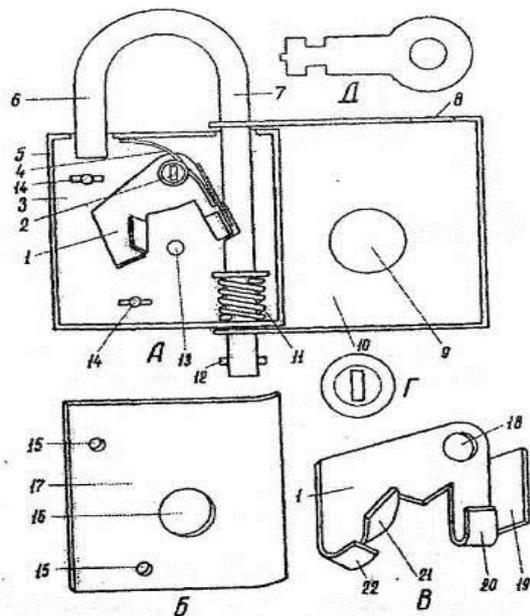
Устройство висячего бессувальдного контрольного замка: А - замок; Б - крышка корпуса; В - засов; Г - ключевина; Д - ключ; 1 - хвостовик засова; 2 - ось засова и пружины; 3 - основание корпуса; 4 - пружина засова; 5 - боковая стенка; 6 - свободный конец дужки; 7 - запираемый конец дужки; 8 - отверстие для свободного конца дужки; 9 - контрольное окно; 10 - дополнительная (контрольная) крышка; 11 - пружина дужки; 12 - ограничитель; 13 - стойка для ключа; 14 - стойка для крепления крышки корпуса; 15 - отверстие для крепления крышки корпуса; 16 - отверстие для ключевины; 17 - крышка корпуса; 18 - отверстие для оси; 19 - упорный выступ для пружины; 20 - головка засова; 21 - выступ для ключа; 22 - стойка, усиливающая выступ для ключа.
